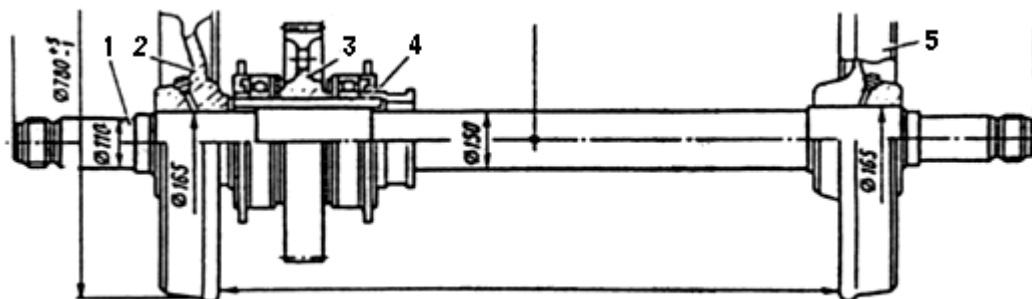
Колісна пара з суцільнокатаними колесами:
